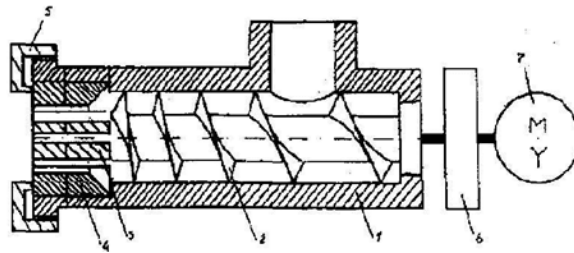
Схема пресса для производства кормовых смесей: 1 - корпус; 2 - шнек; 3 - формующая головка; 4 - втулка; 5 - зажимная гайка; 6 - редуктор; 7 – электродвигатель.
